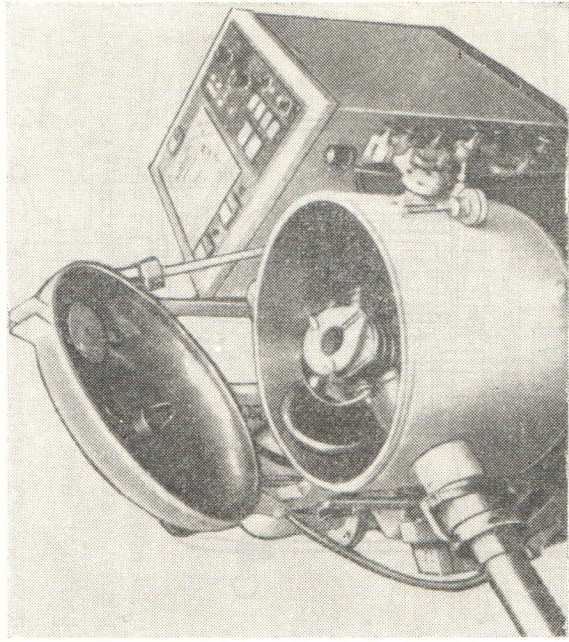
Вакуумная индукционная лабораторная печь с вертикальным металлическим корпусом
